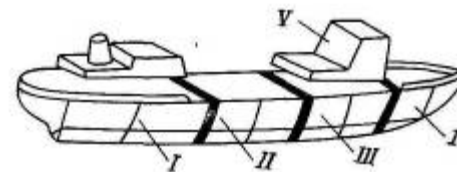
Блочный метод постройки судна. I—IV—блоки корпуса; V—блоки надстроек.
